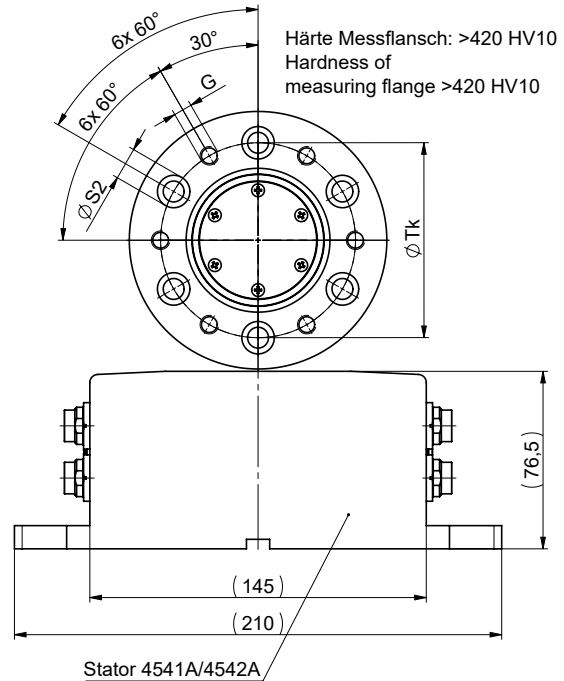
Maßzeichnung Ansicht B, KiTorq System
